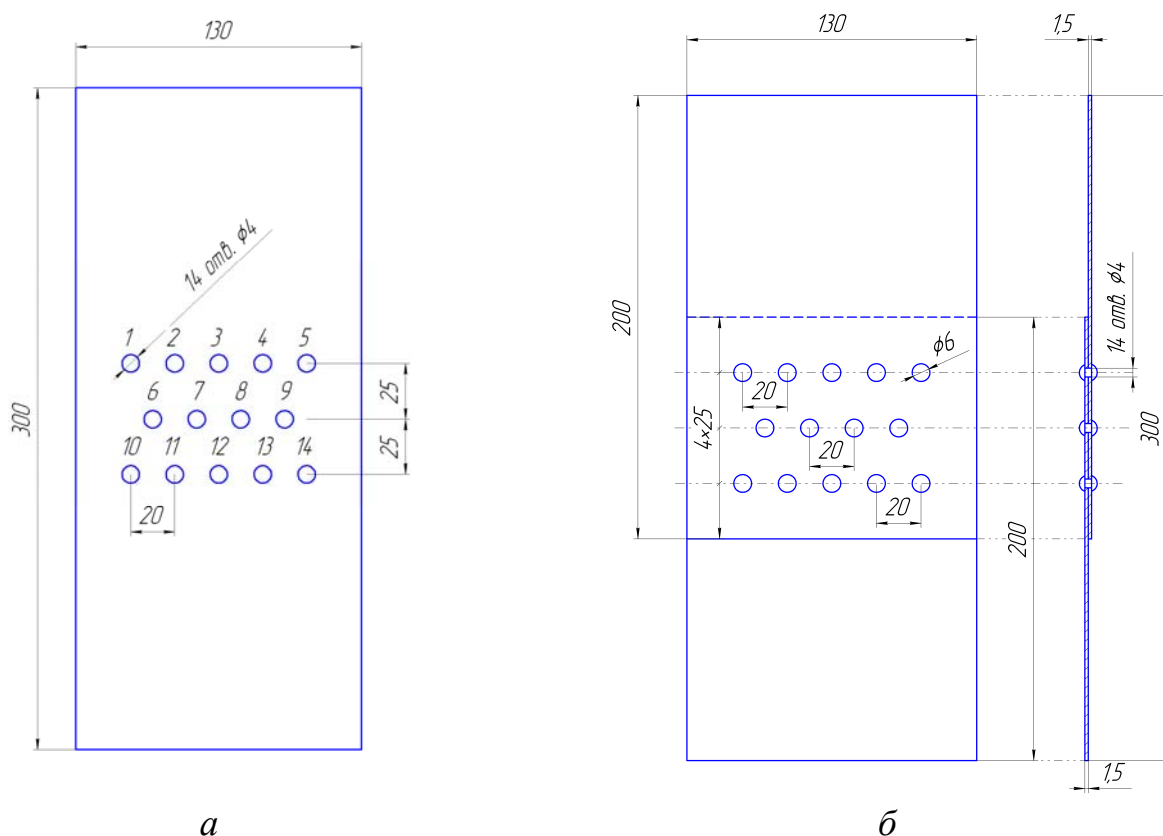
Образцы для испытаний: а – сплошной образец с отверстиями под заклёпку; б – заклёпочное соединение, моделирующее фрагмент обшивки ЛА
